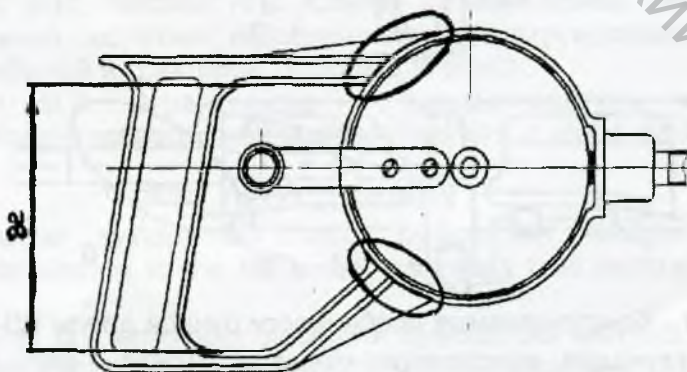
Общий вид крепления рукоятки к корпусу
